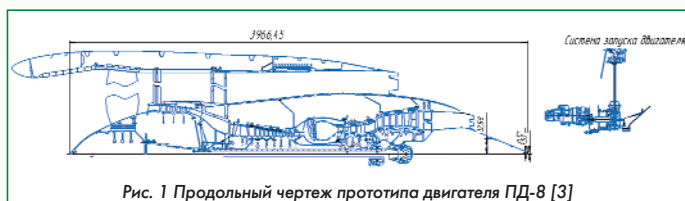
Продольный чертеж прототипа двигателя ПД-8 [3]
